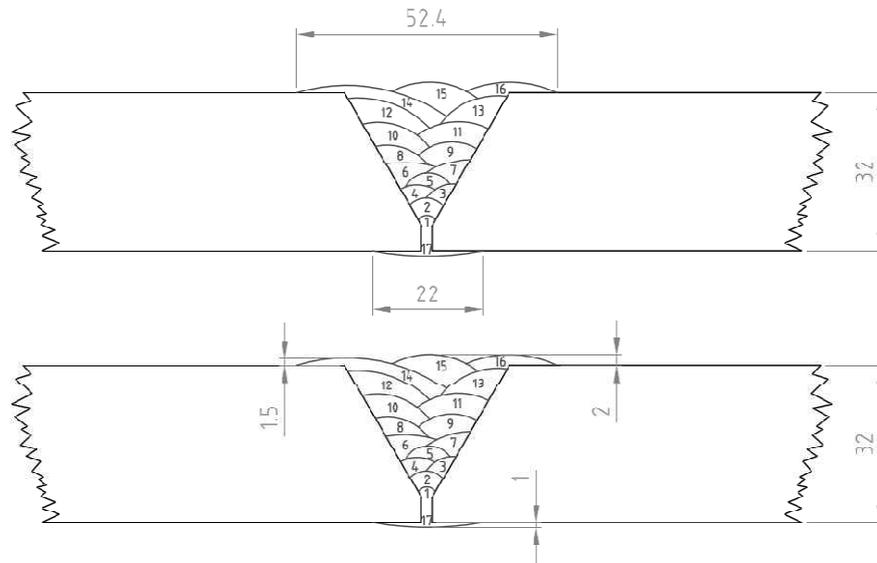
Tamaño de Cordón de Soldadura
